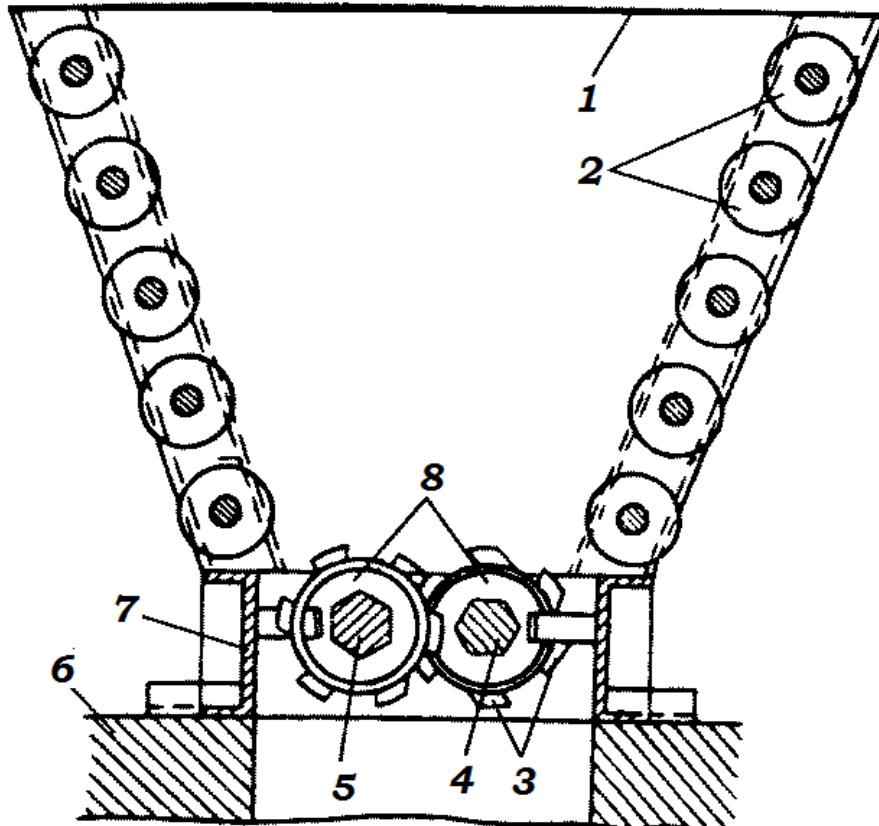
Роторно-дисковая дробилка для дробления крупногабаритных отходов:
